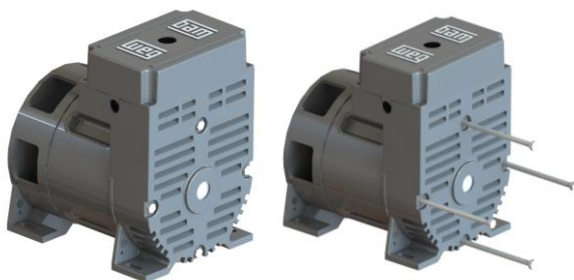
Position de la tête des tirants dans le couvercle arrière
